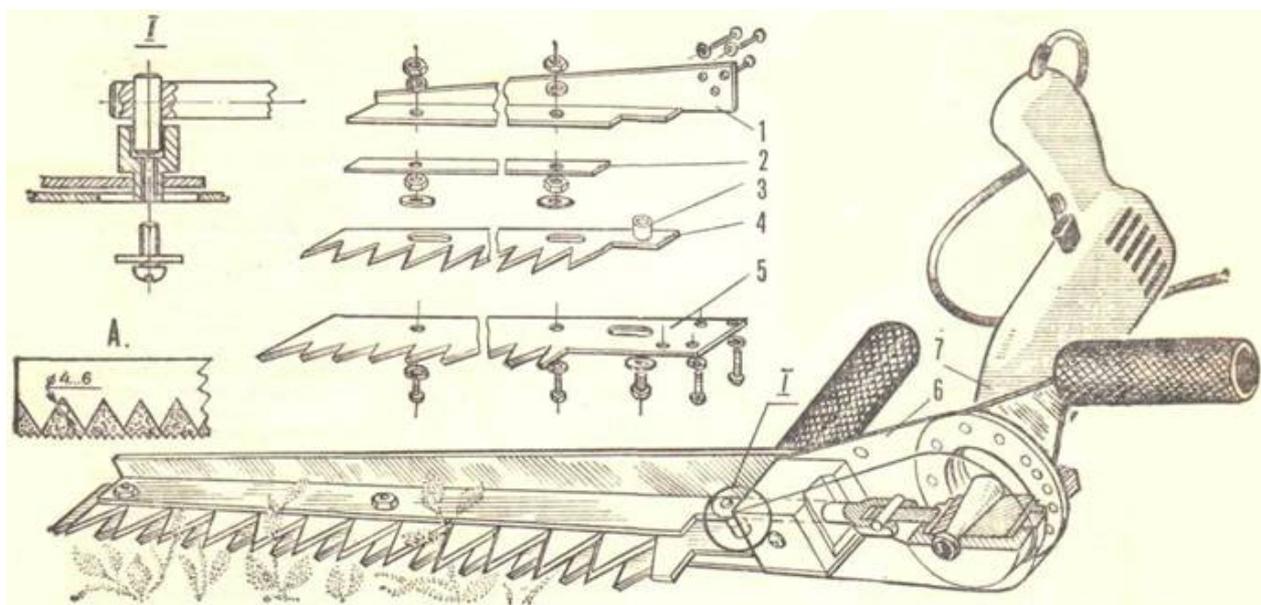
Конструкция косилки и основные детали режущего аппарата:
